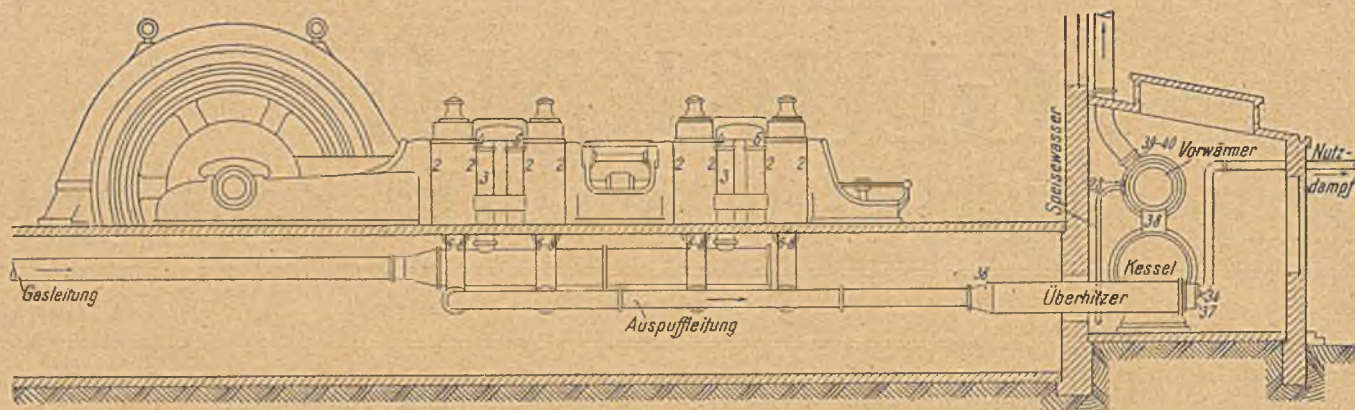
Aufriß der Gasmaschine mit Abwärmekessel.
